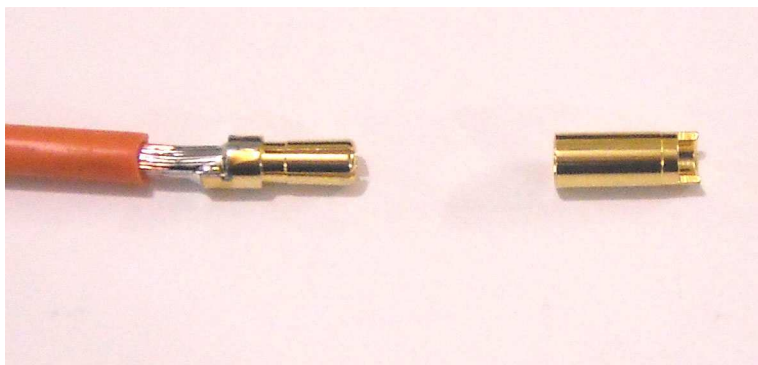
Une prise PK 5.5 mm soudée à un câble de 10mm².
